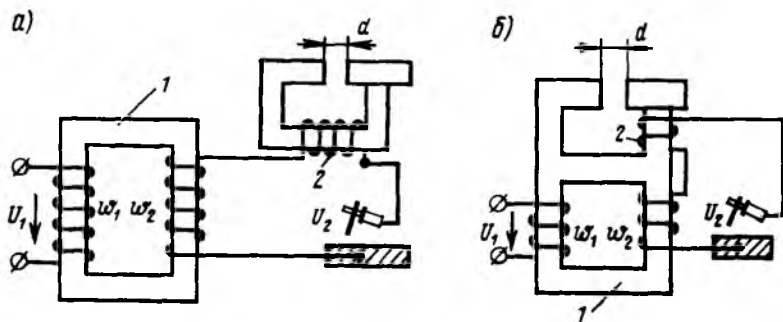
Принципиальные схемы сварочных трансформаторов.
